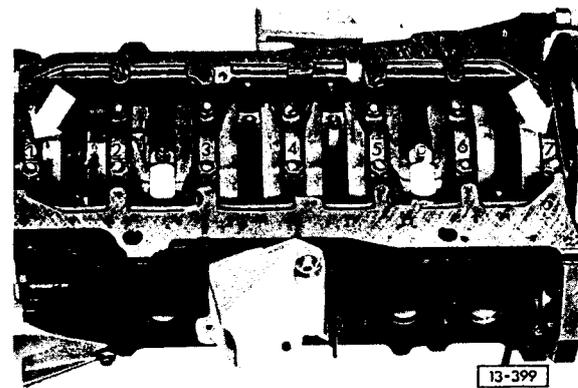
Vilebrequin-Chapeaux de palier: position de montage
